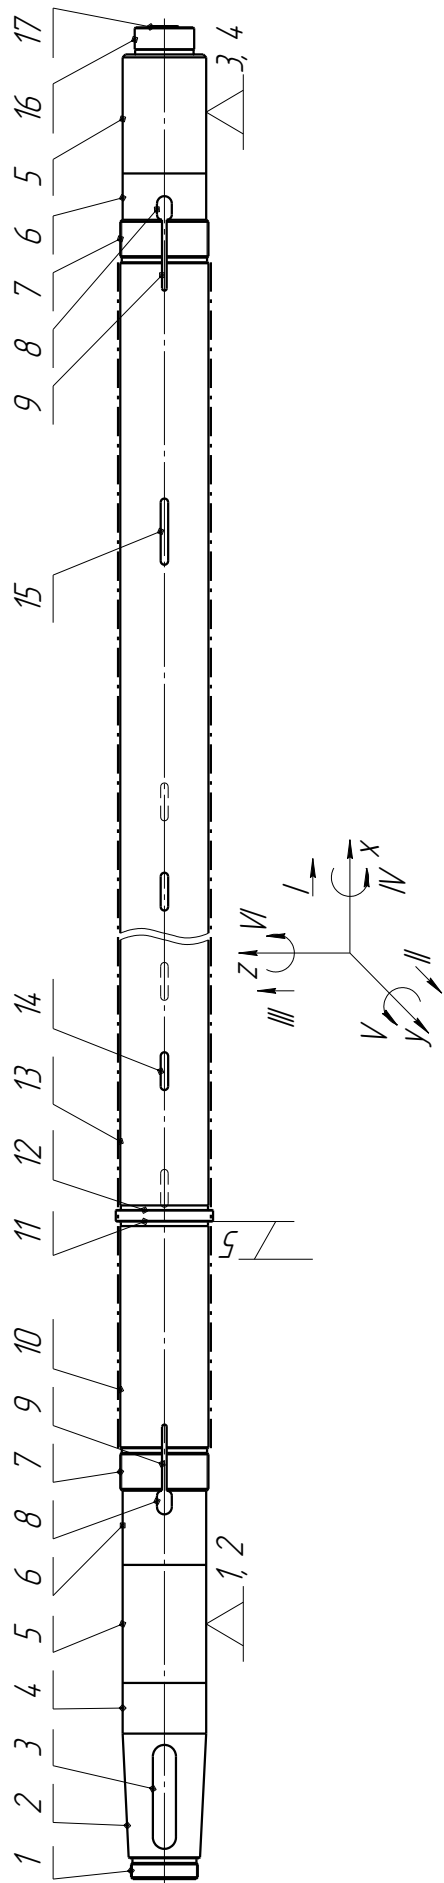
Эскиз вала с указанием поверхностей и конструкторских баз
